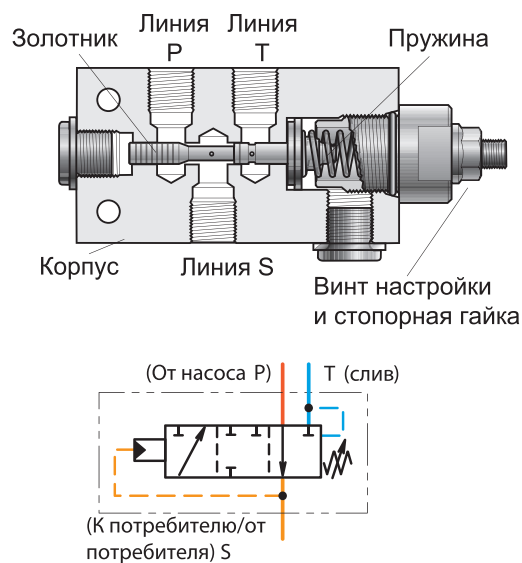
Трёхлинейный редукционный клапан (в разрезе) со схемой
